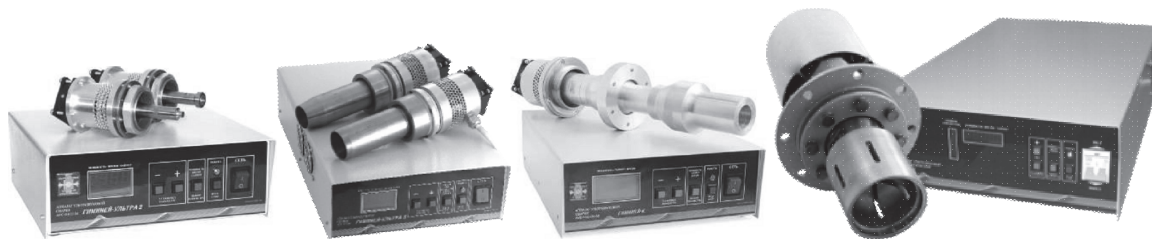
Сварочные аппараты для прессовой сварки кольцевых швов
